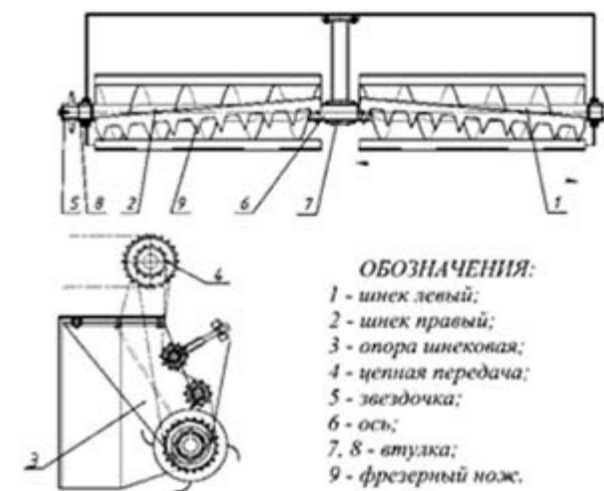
Грунтозаборное устройство фрезерно-шнекового типа для разработки торфа
